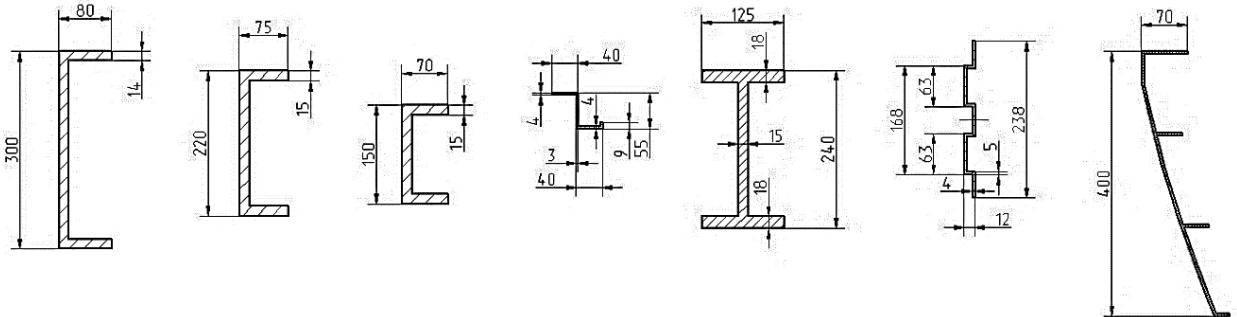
Прессованные профили из алюминиевых сплавов, применённые при изготовлении кузова вагона ЦМВОА-69
